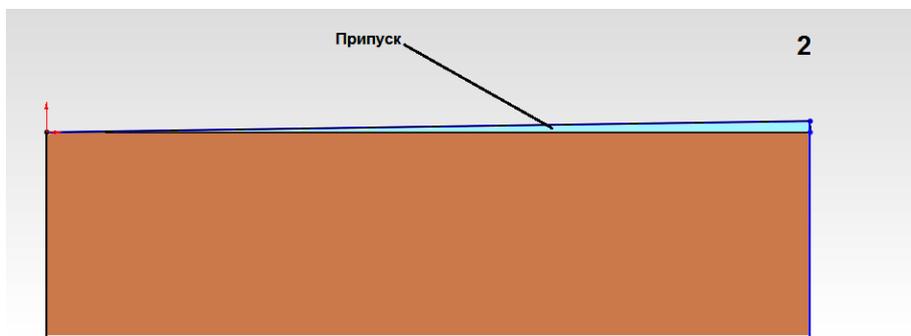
Формообразование поверхностного слоя одним зубом зубообрабатывающей фрезы
